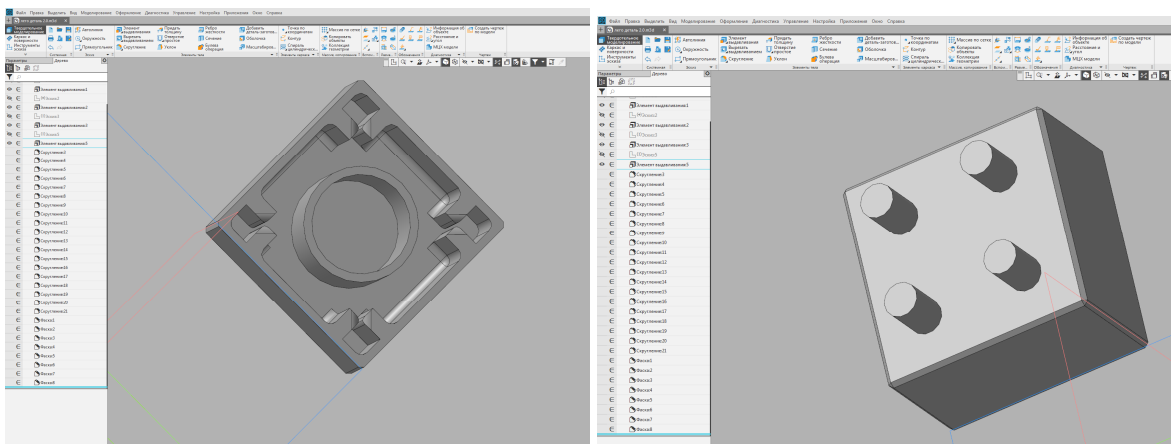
Создание чертежа и трехмерной модели блока конструктора Лего
